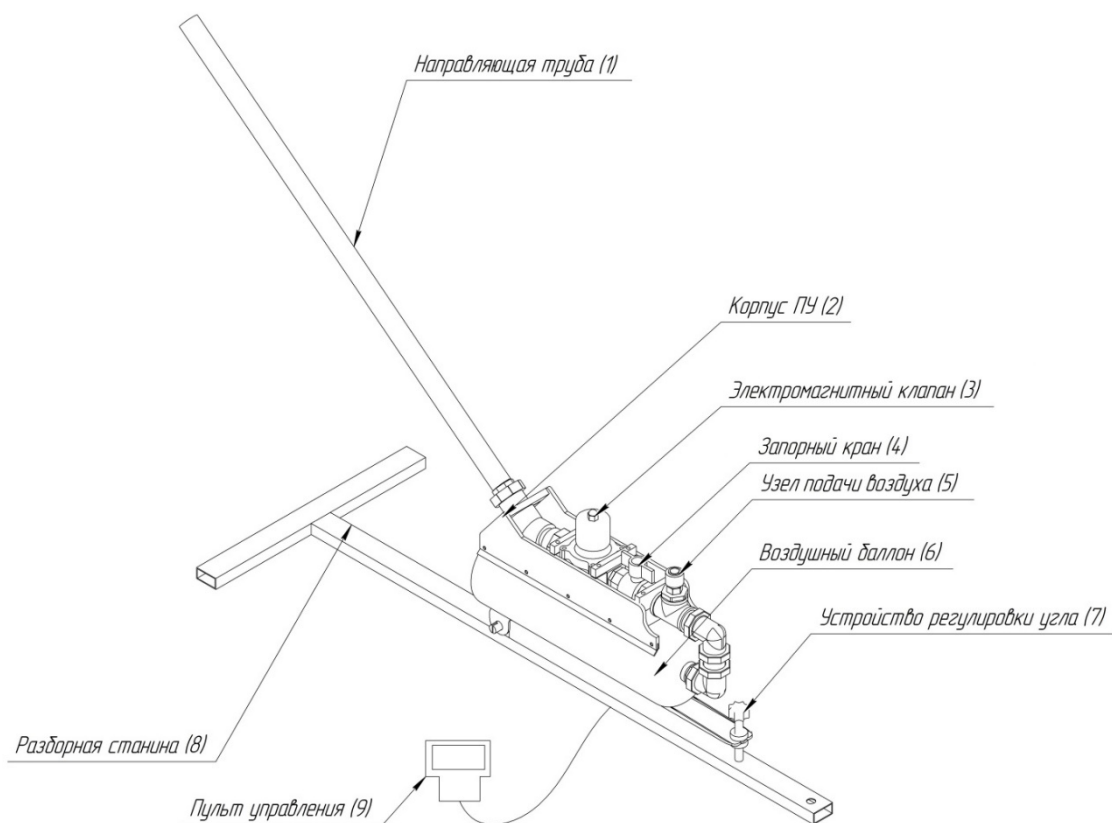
Общий вид пусковой установки минометного типа
